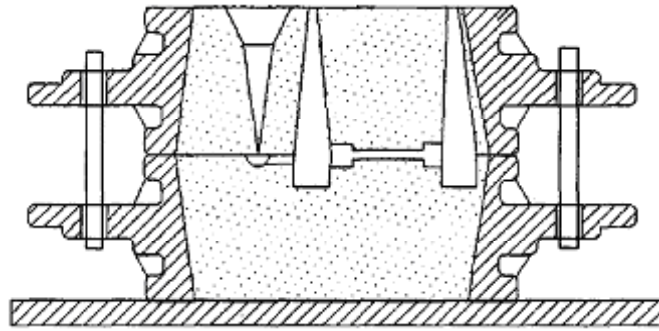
Схема ливарної форми для одержання зразків
